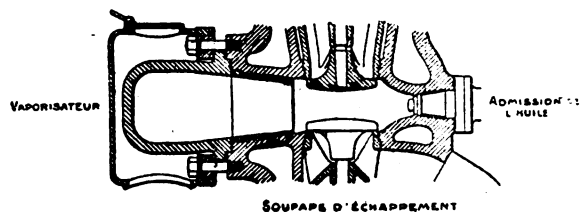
Chambre de combustion du moteur De la Vergne.
